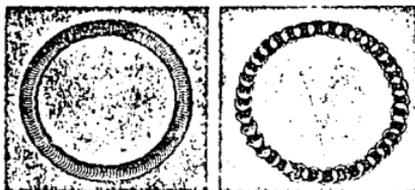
Soldaduras por costura hechas con puntos sobrepuestos de separación variada.
